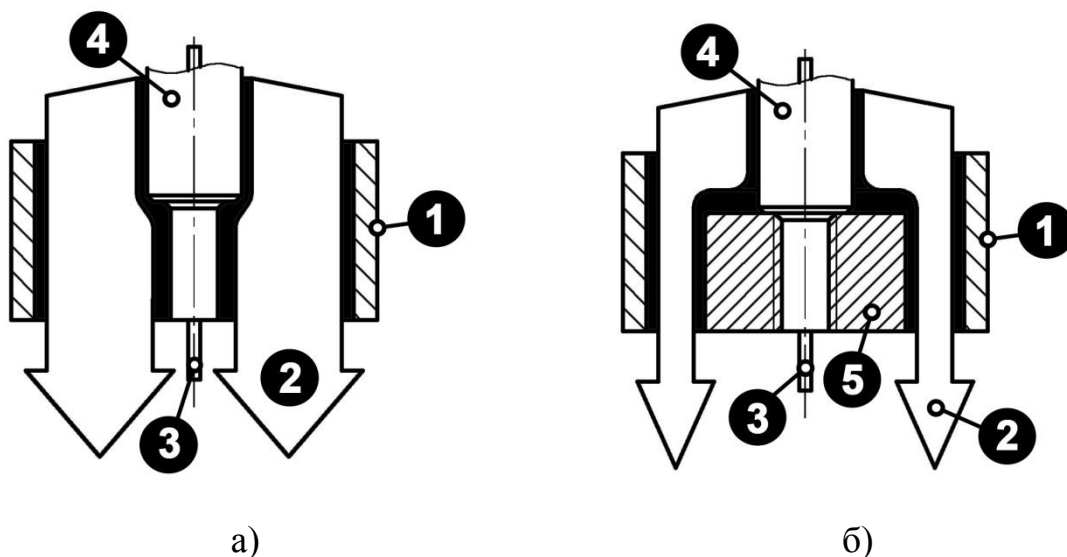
Схемы подачи защитного газа в зону сварки при традиционном и комбинированном способе газовой защиты: 1 – сопло сварочной горелки; 2 – поток защитного газа (CO_2); 3 – электродная проволока; 4 – токоподводящий наконечник; 5 – втулка для распределения газового потока (а – схема с традиционной подачей защитного газа в зону сварки; б – схема с кольцевой подачей защитного газа)
